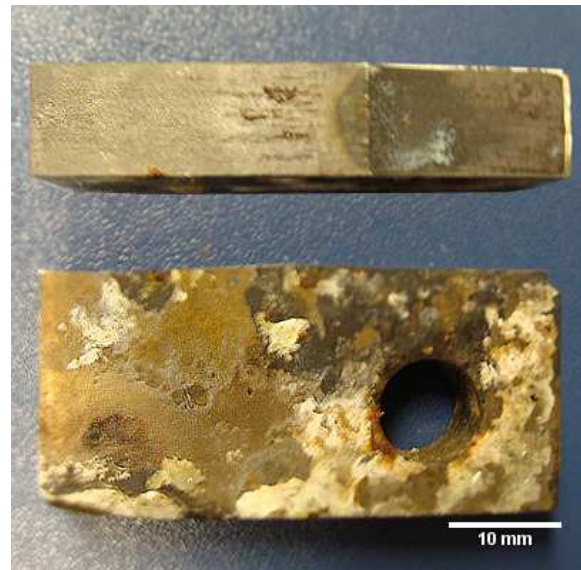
Superfície de fratura do corpo de prova metal de solda 1 fraturado no ensaio de tenacidade a fratura em meio agressivo.
